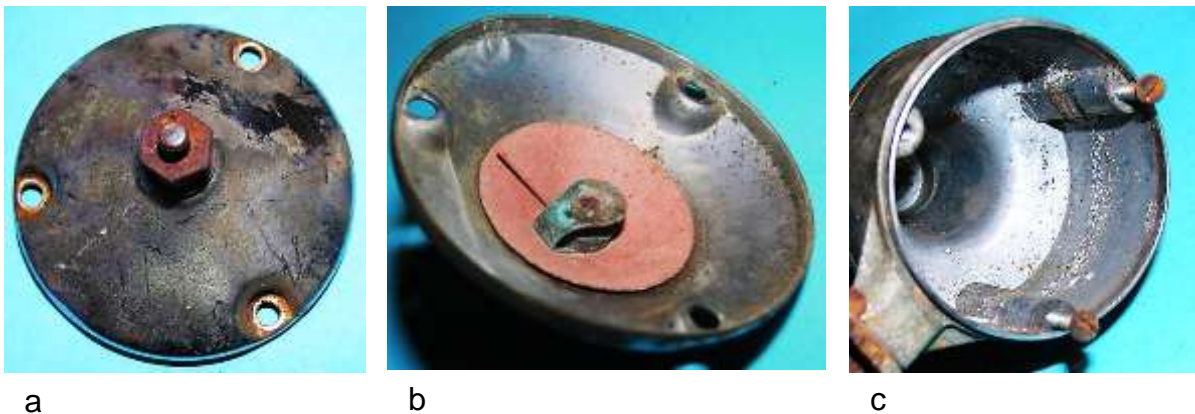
Gehäuseteile: a) Außenansicht des Bodens, b) Innenansicht des Bodens mit Spannung führender Blattfeder, c) Innenraum des Gehäuses mit angegossenen Stegen
